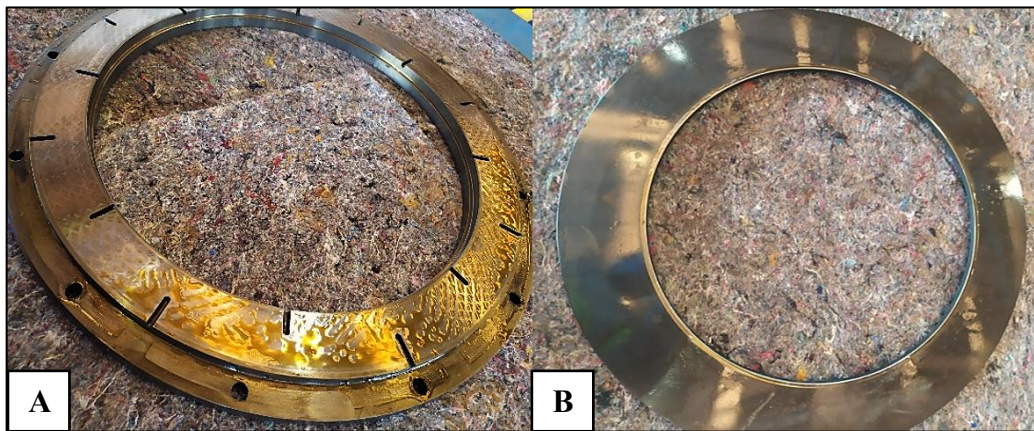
Fixador (A) e pistão (B) do conjunto de direção da embreagem.
